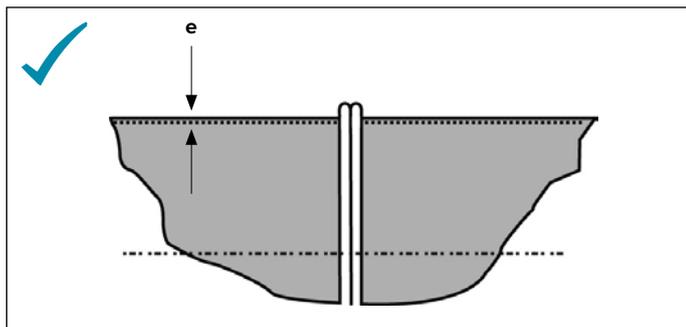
Ligne de soudure avec une formation de bourrelet régulière (OK)
